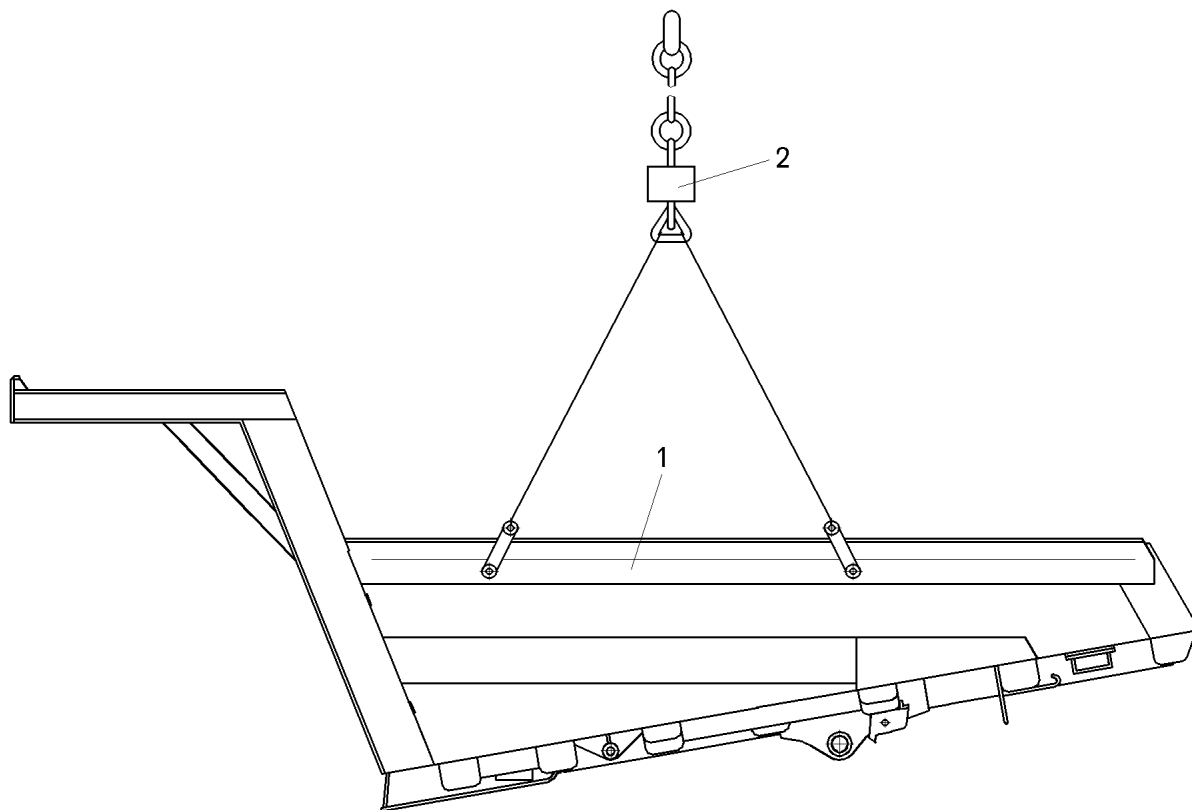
Схема снятия и установки платформы самосвала:
